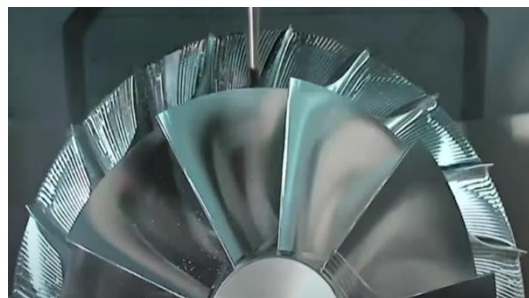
Ukázkový model na 4D „Pocet clearing“ obrábění
